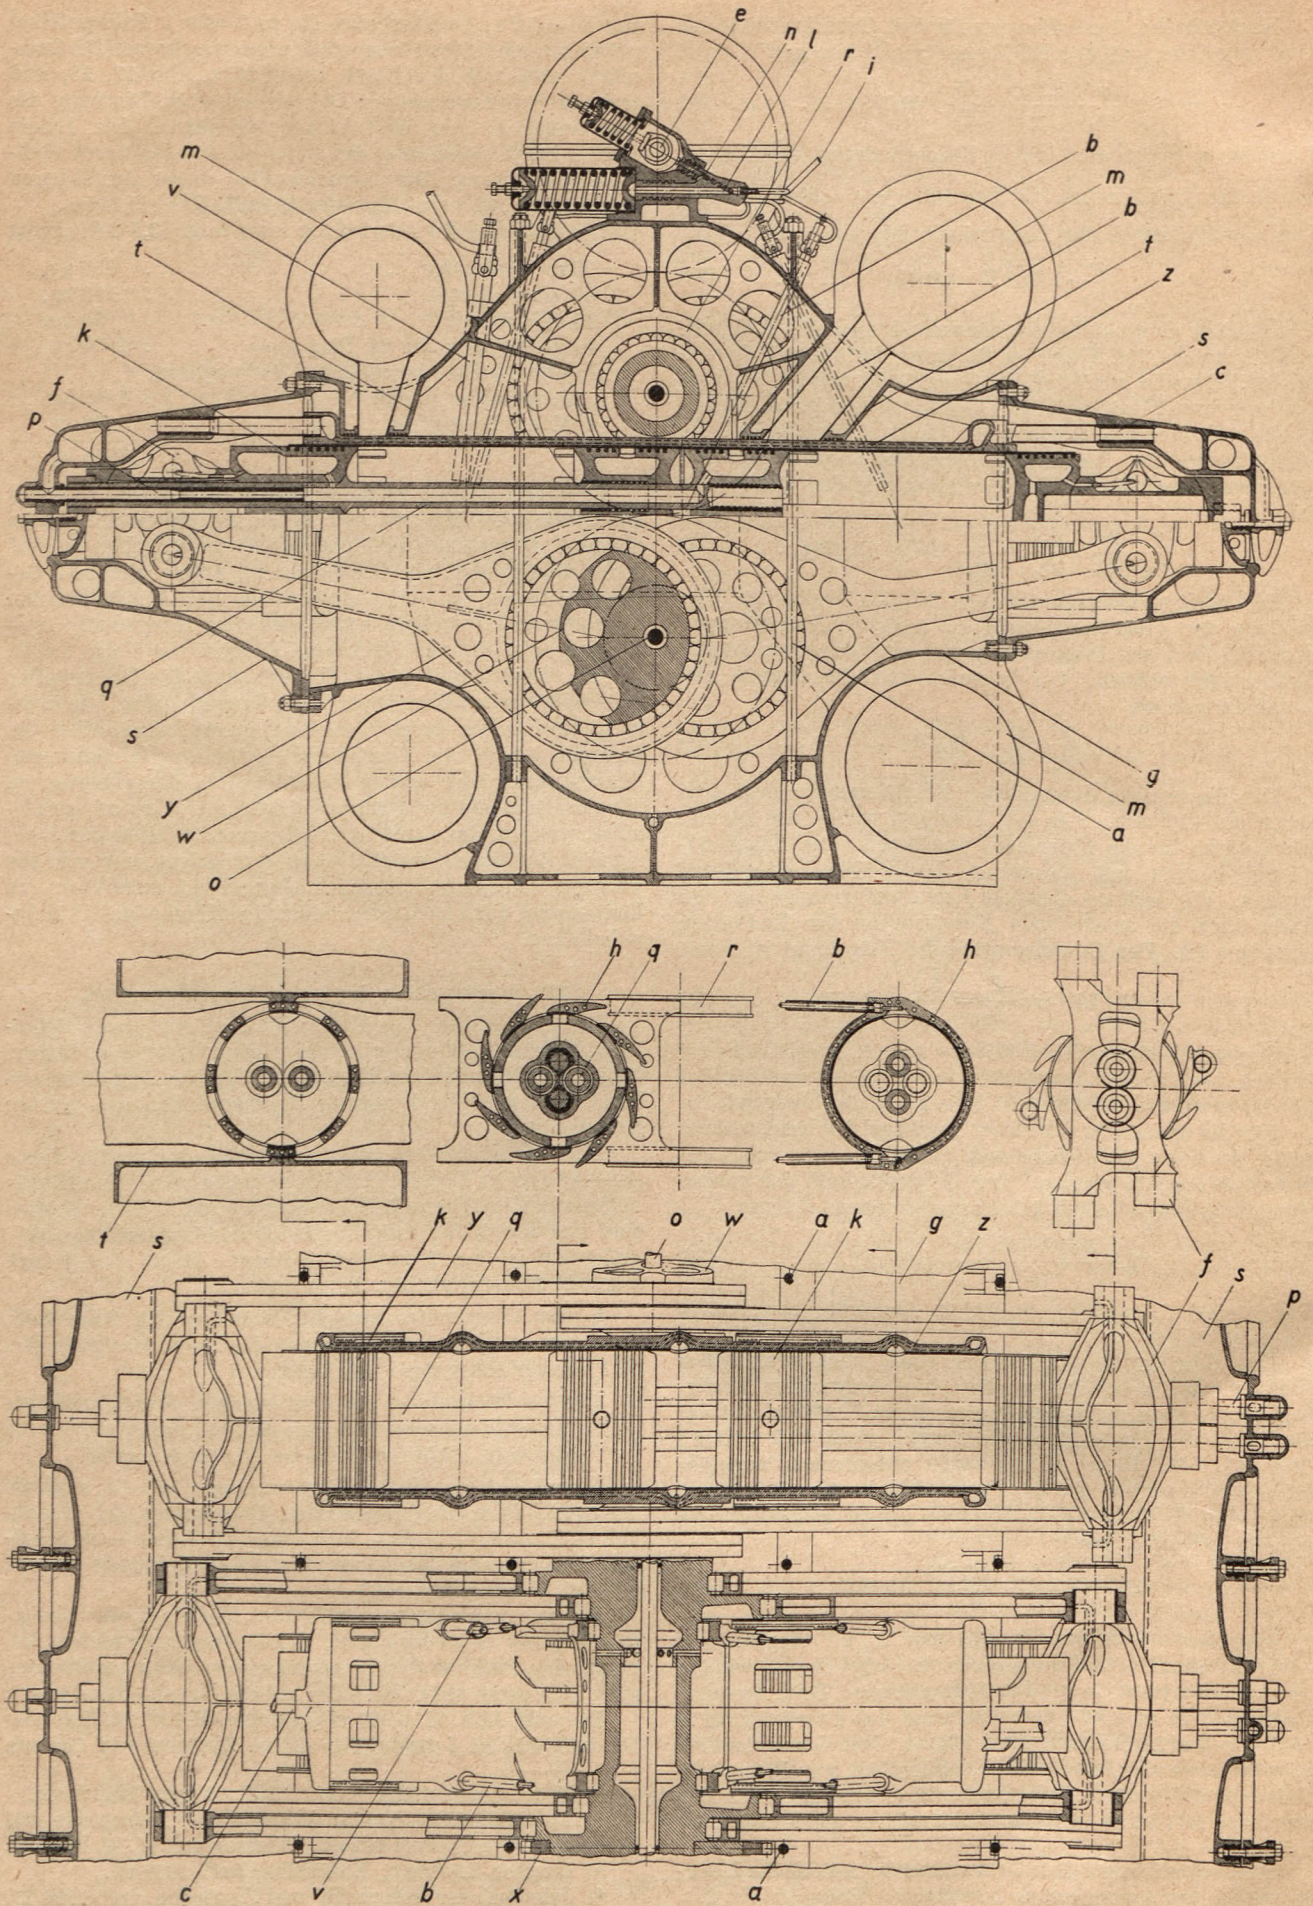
u. 12. Maßstab 1:7,5, Dieselflugmotor von 1250 PS; 6 Zylinder von 132 mm-Bohrung mit Gegenkolben von 2×106 mm Hub; 1875 U/min.
